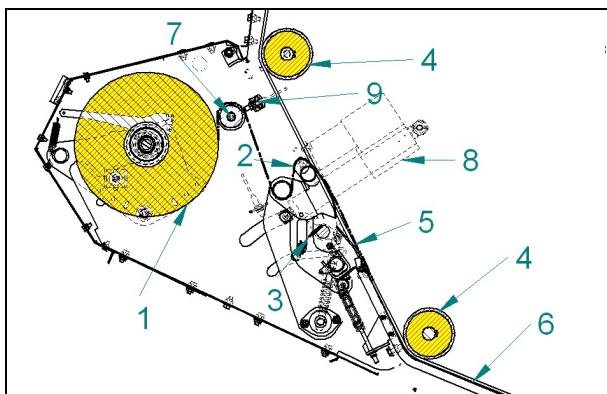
Obwiązywacz przygotowany do owijania beli.
